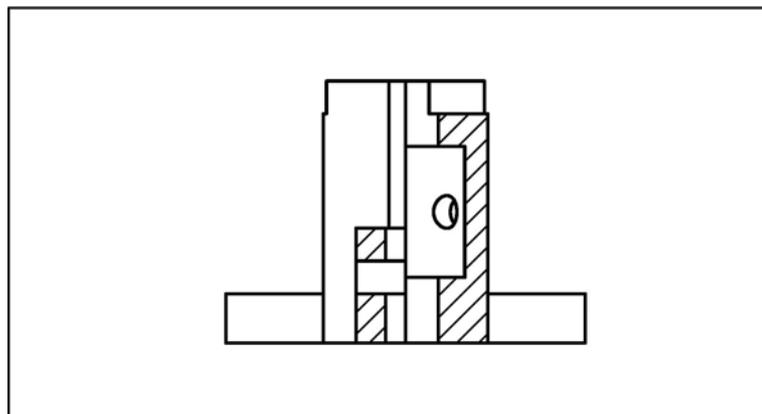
Сложный ступенчатый разрез, полученный командой SECTIONPLANE
